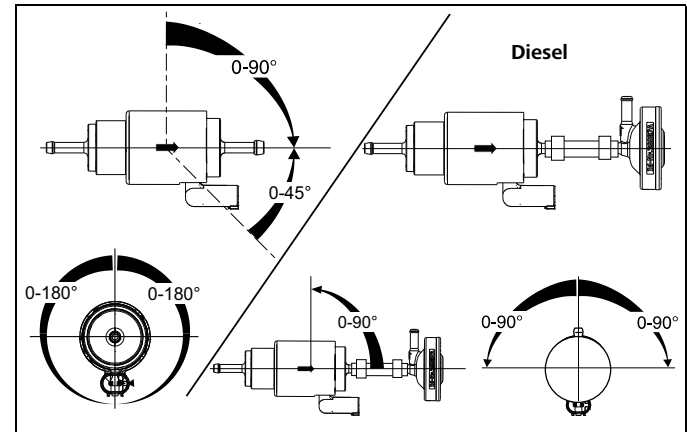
Brennstoffpumpe DP 42 Einbaulage
